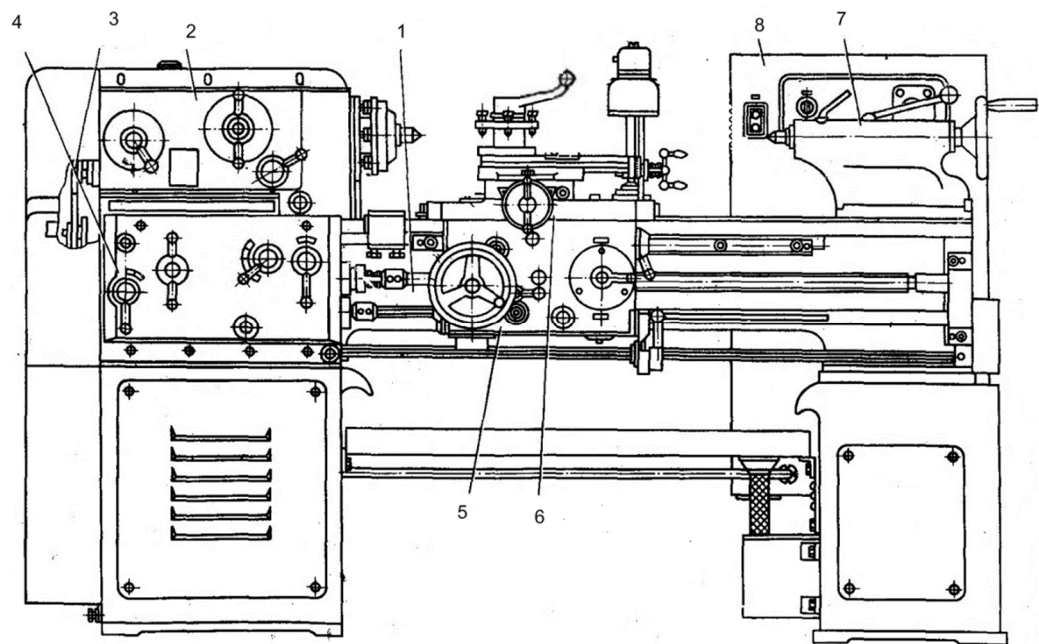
Основні частини токарно-гвинторізного верстата моделі 1K62
